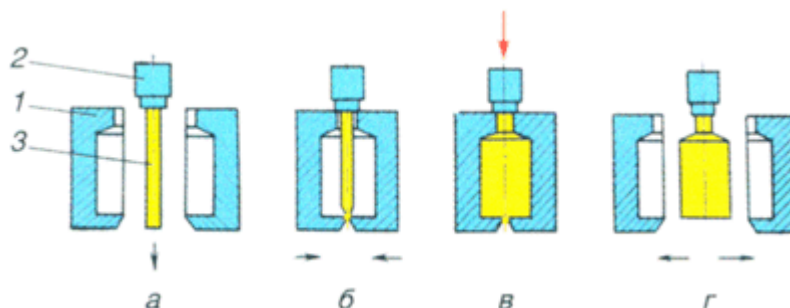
Схема экструзионно-выдувного формования [17]: 1 – пресс-форма; 2 – трубная головка; 3 – трубная заготовка
